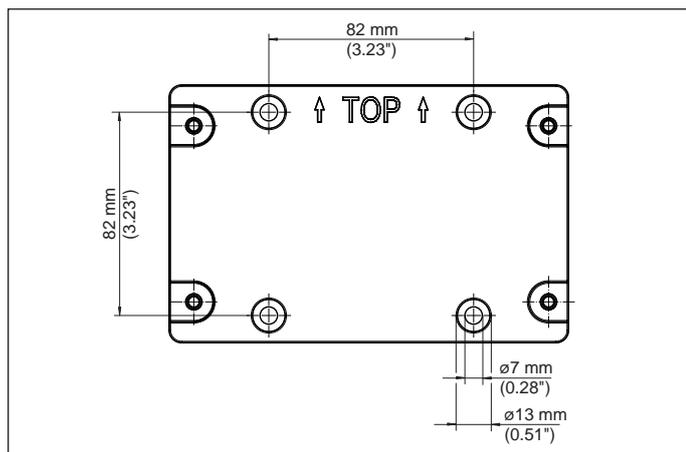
Placa de montaje para montaje en pared (VEGAMET 841, 842)
